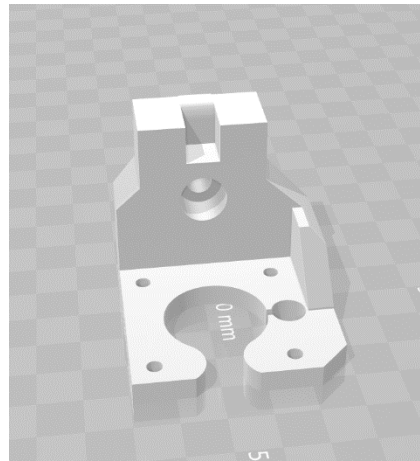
Uchycení motoru horní pravé Autor: David Trcka
